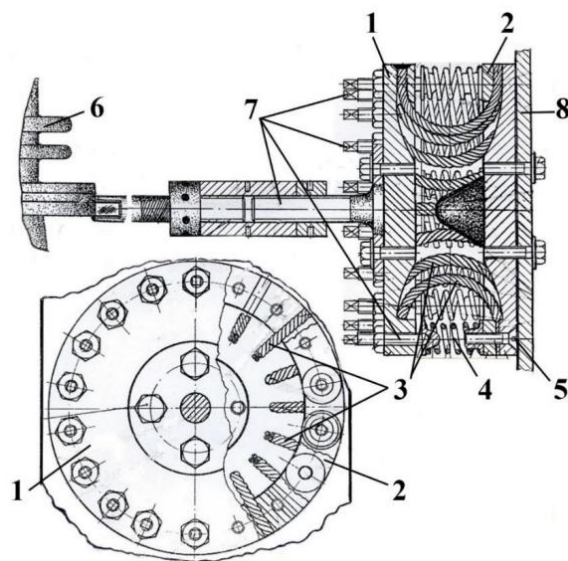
Пружинно-канатний упор поперечних коливань
